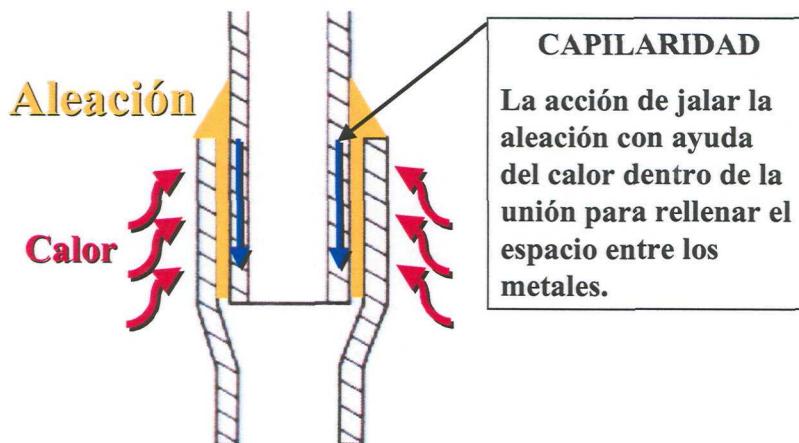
Acción de la capilaridad en la soldadura de tubería.
